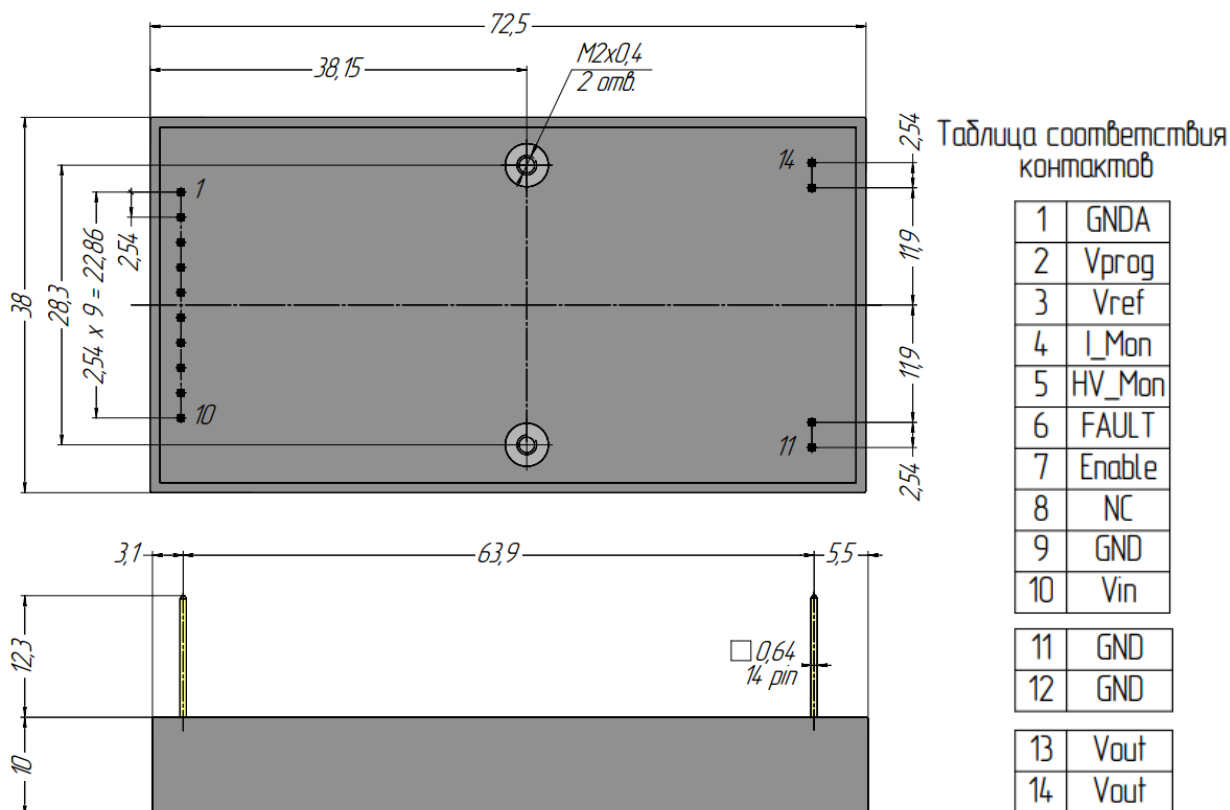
Чертеж и внешний вид источника питания серии HVLP в пластиковом корпусе
